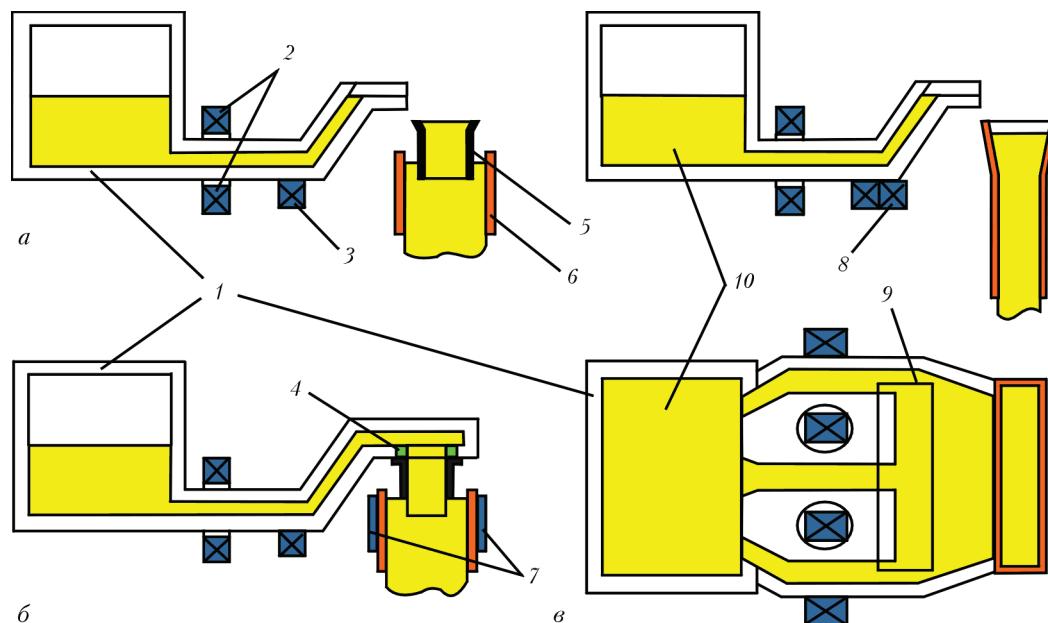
Схема разливки стали через многофункциональный МД-ПК с применением электромагнитных воздействий: *а* — полунепрерывная разливка; *б* — непрерывная разливка сортовой заготовки и бломов; *в* — непрерывная разливка тонкого сляба; 1 — МД-ПК; 2 — индуктор; 3 — электромагнит для создания электромагнитной силы, обеспечивающей перемешивание и разливку стали; 4 — герметизирующая прокладка; 5 — погружной стакан; 6 — кристаллизатор; 7 — пульсационный ЭМП; 8 — электромагнитное устройство для рассредоточения струи стали по ширине сляба в кристаллизаторе; 9 — зона создания электромагнитной силы при разливке металла из ПК в кристаллизатор тонкослябовой МНЛЗ; 10 — жидкая ванна
